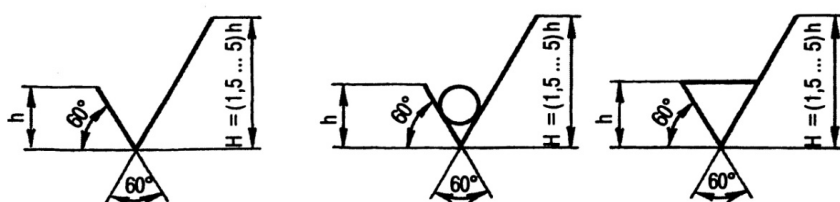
Знаки, применяемые для обозначения шероховатости
